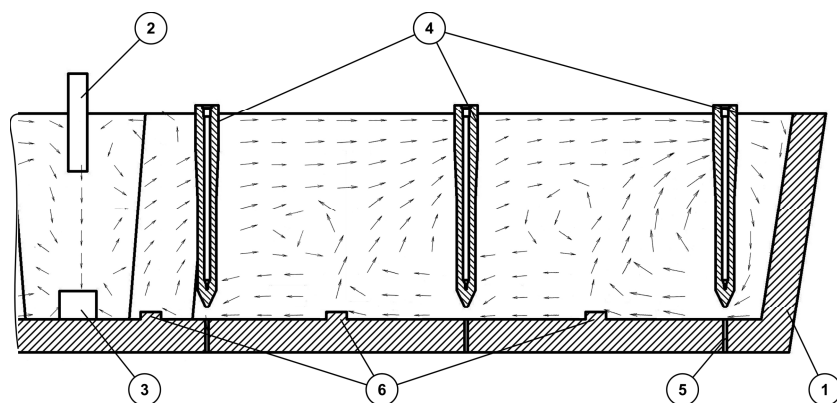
Схема циркуляционных потоков жидкой стали в проковше МНЛЗ предложенной конструкции: 1 – проковш; 2 – защитная труба; 3 – турбостоп; 4 – стопоры; 5 – разливочный стакан; 6 – продувочные блоки
